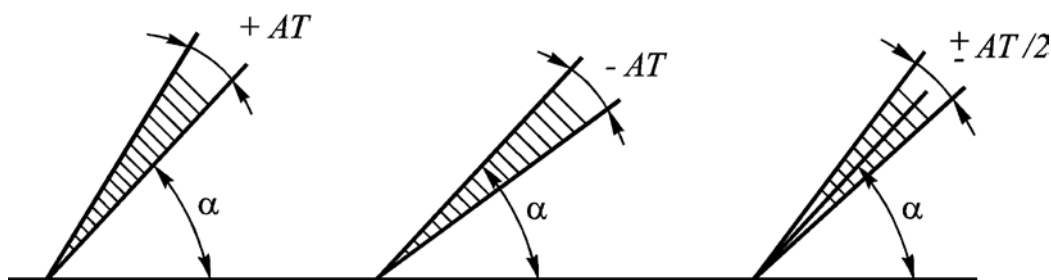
Варианты расположения поля допуска угла относительно номинального размера угла:
